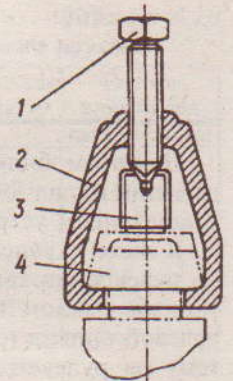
Съемник сошки рулевого механизма: 1 - винт; 2 - захват съемника; 3 - вал сошки; 4 - сошка
